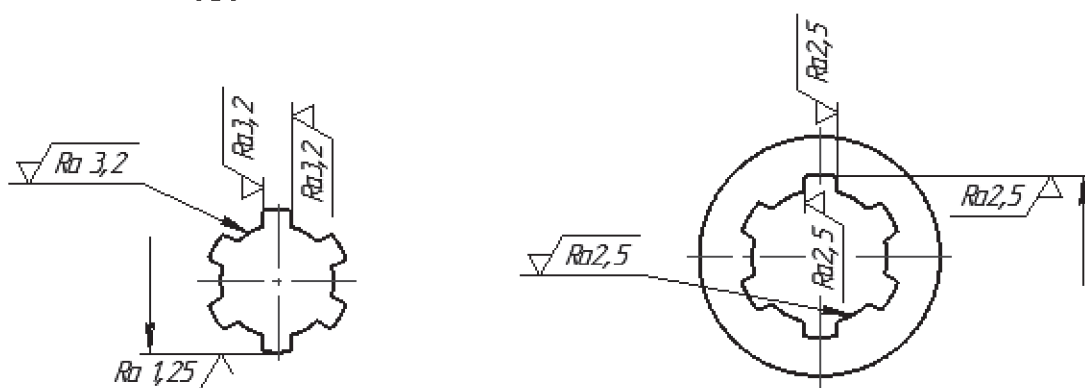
Обозначение шероховатости поверхности на прямобочных шлицах
